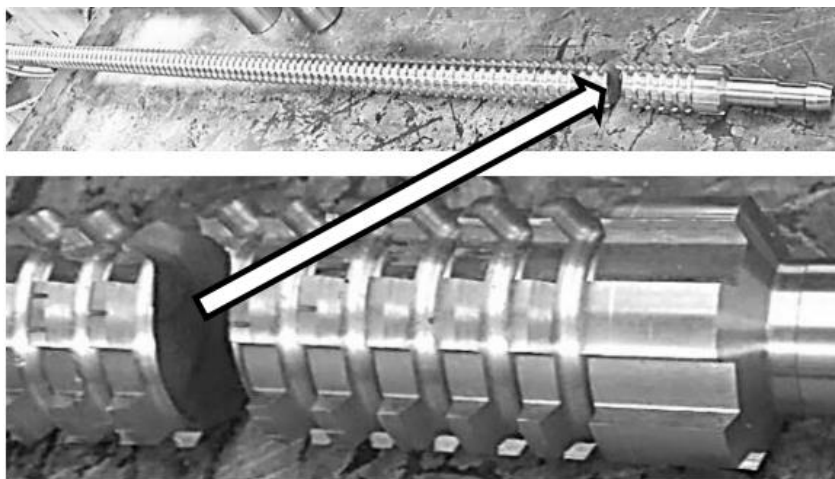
Руйнування протяжки під час вигинання через неперпендикулярність торця деталі до її внутрішньої поверхні [4]
